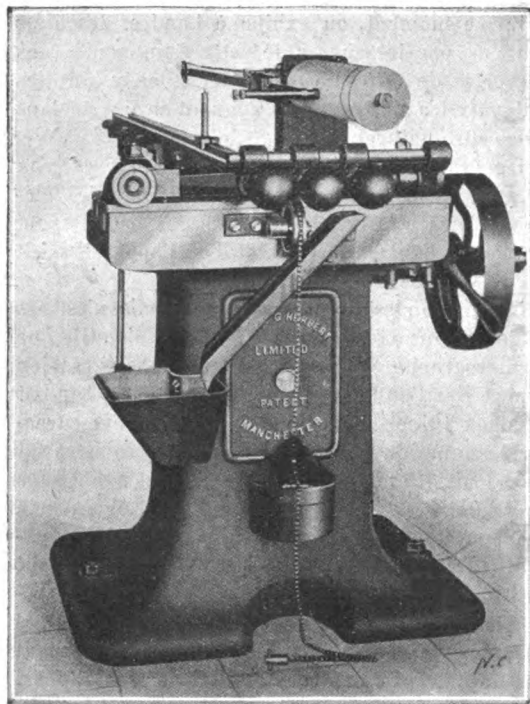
MACHINE POUR ESSAIS DES LIMES.
